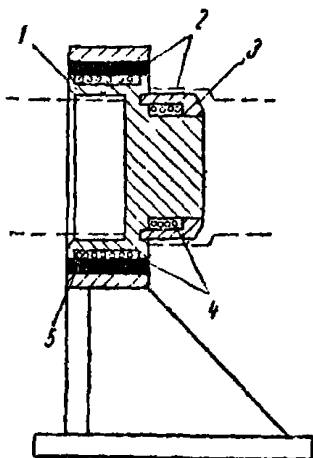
Приспособление для нагрева гладких концов и раструбов деталей из труб
